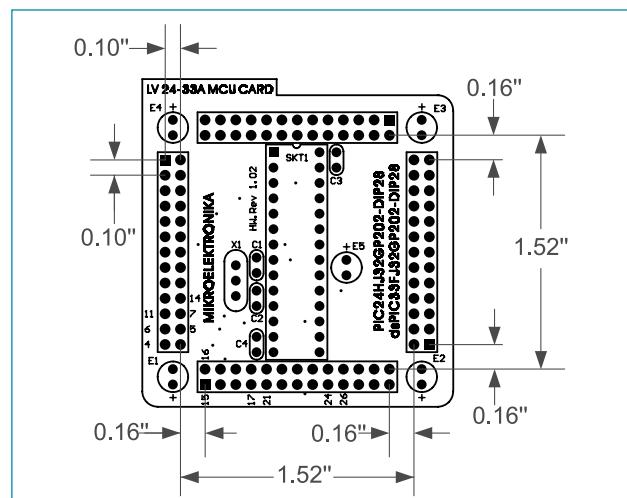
Dimensiones de la tarjeta MCU para la *MCU Card 11
